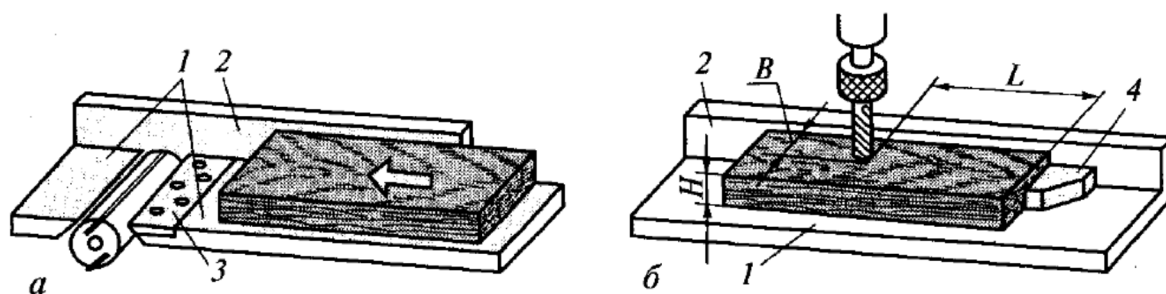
Рухоме (а) та нерухоме (б) базування заготовок при деревообробці:
